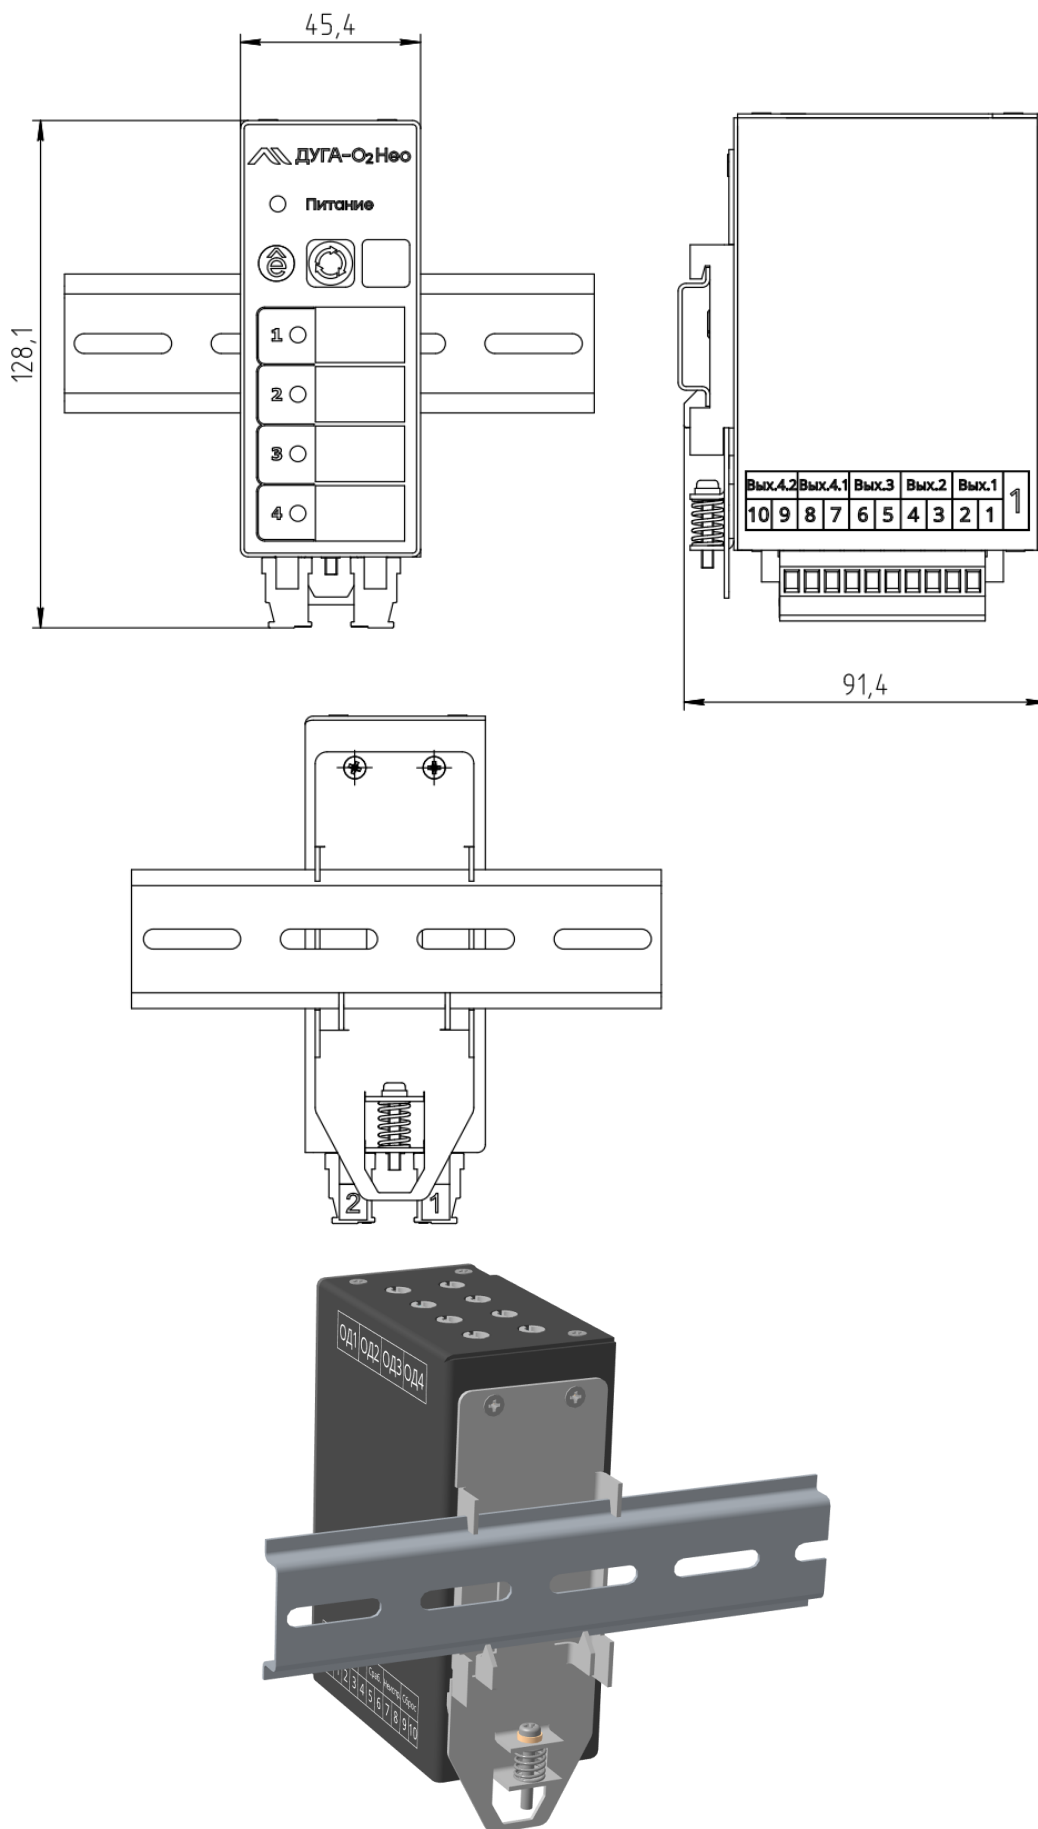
Габаритные размеры и внешний вид регистратора
